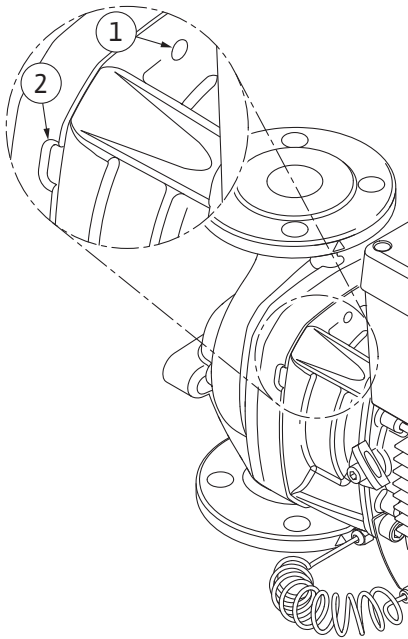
Gewindebohrungen und Schlitze zum Abdrücken des Einstecksatzes vom Pumpengehäuse
